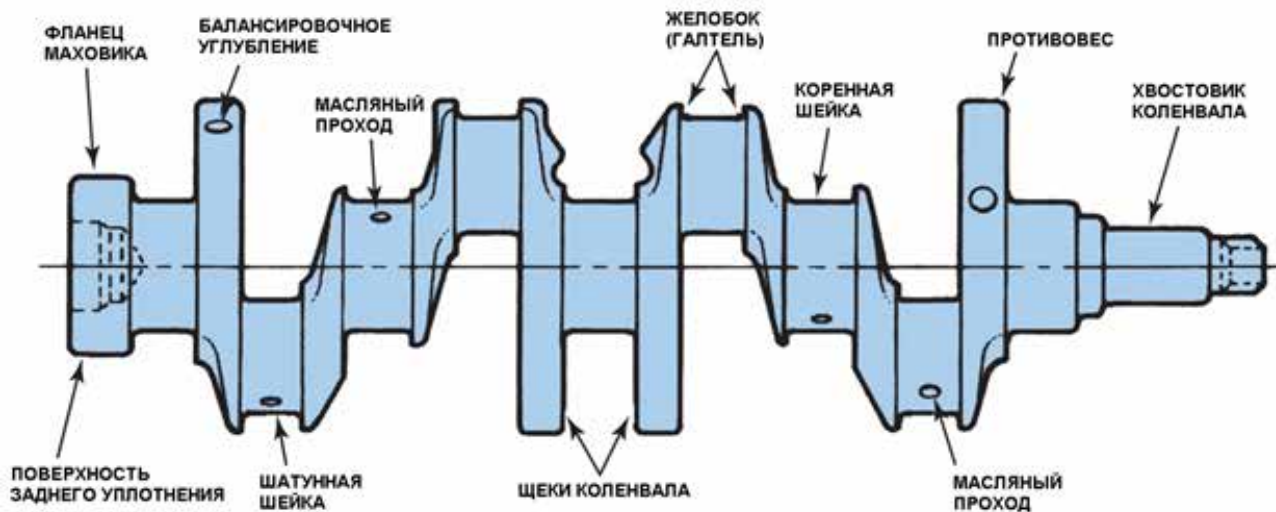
Типичный коленчатый вал с коренными шейками, опирающимися на вкладыши коленных подшипников, уложенных в постели блока цилиндров. Шатунные шейки смещены относительно оси вращения коленчатого вала, образуя так называемый радиус кривошипа; источник: *Pearson Education, Inc.
